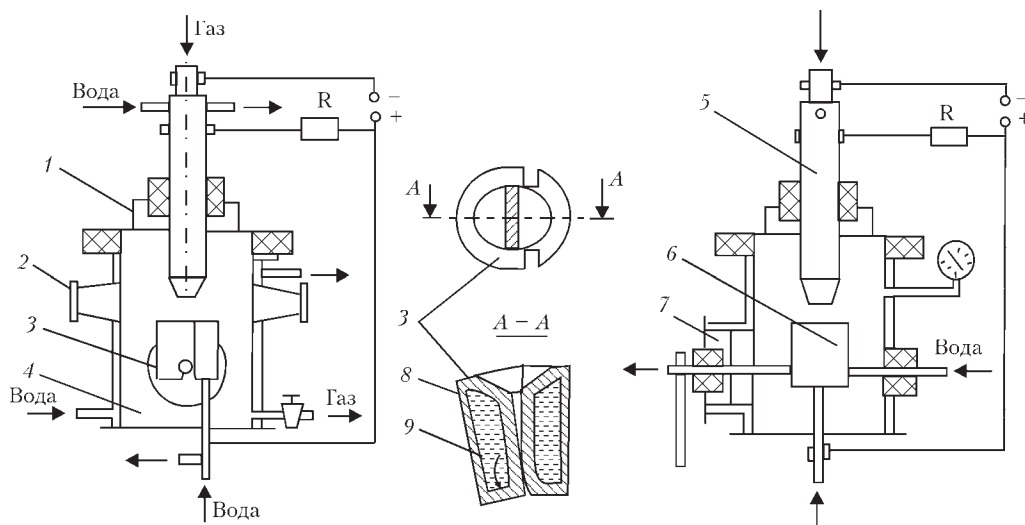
Принципиальная схема плазменно-дуговой установки УПИ: 1 — съемная крышка; 2 — смотровое окно; 3 — раскрывающийся кристаллизатор; 4 — плавильная камера; 5 — дуговой плазматрон; 6 — расплавленный образец металла; 7 — фланец; 8 — закристаллизовавшийся образец металла; 9 — ось поворота подвижного элемента кристаллизатора
